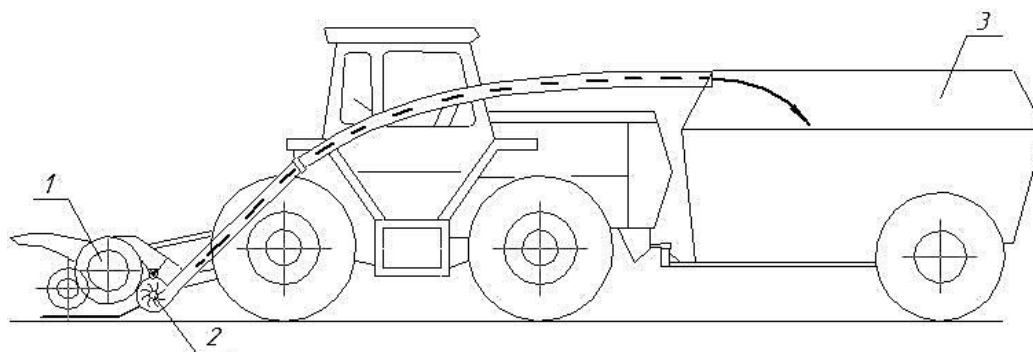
Полевая машина для уборки сои методом очеса: 1 — очесывающая жатка для уборки сои; 2 — система пневмотранспортировки; 3 — прицеп
